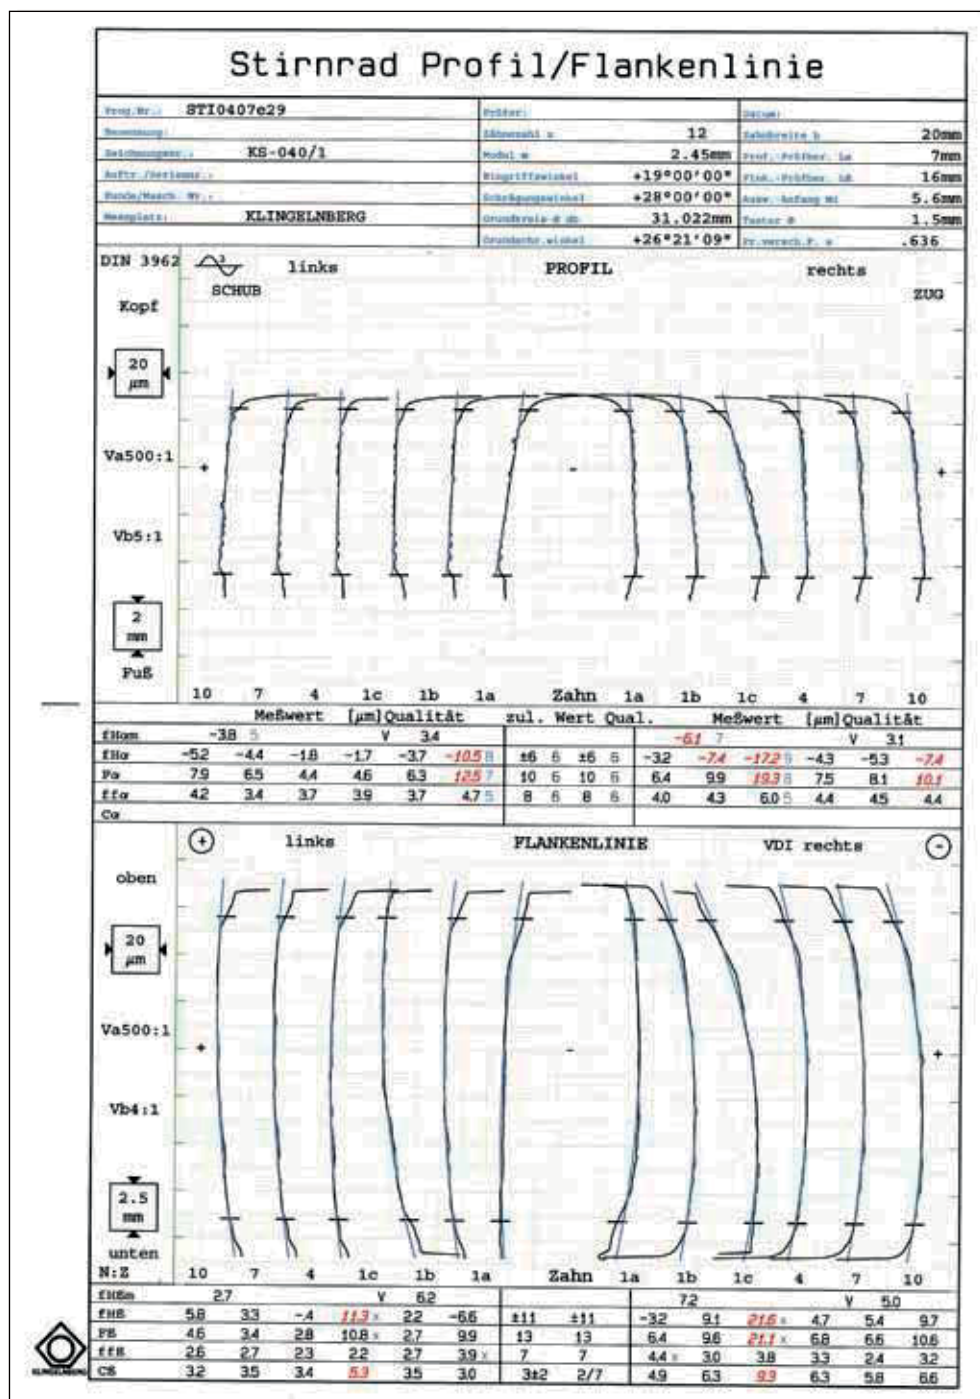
Messprotokoll der Profil-Flankenlinienmessung
